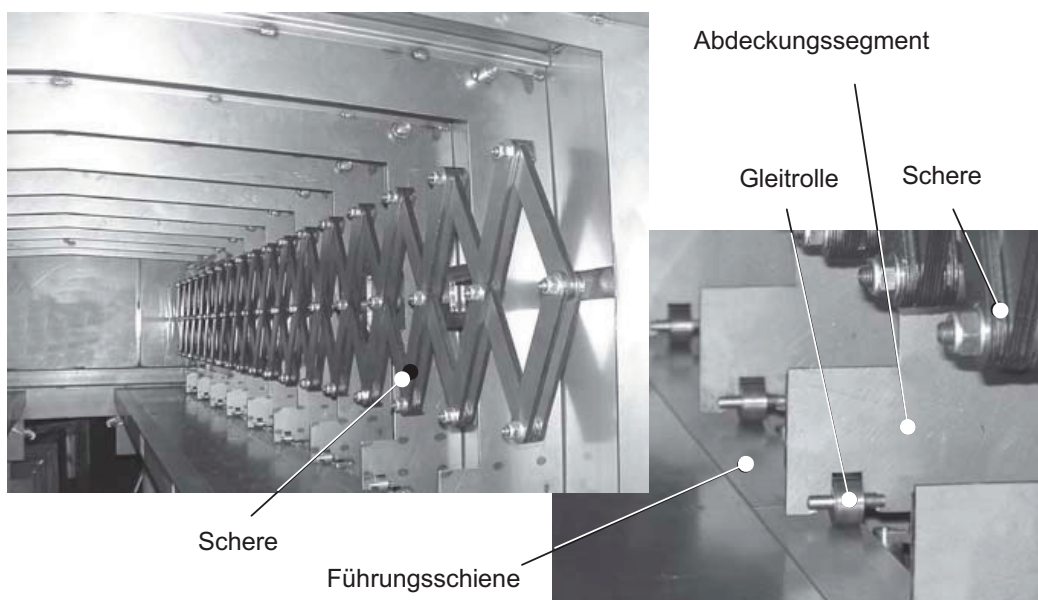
Teleskopabdeckung einer Werkzeugmaschine. Quelle: Kabelschlepp
